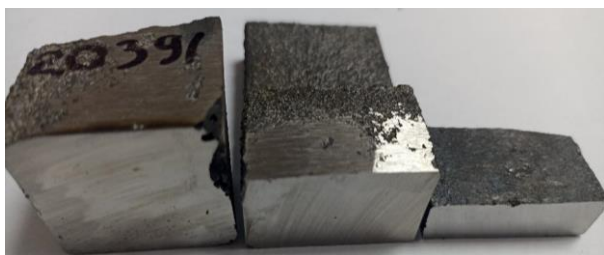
Пробы от различных сечений трехступенчатой отливки
